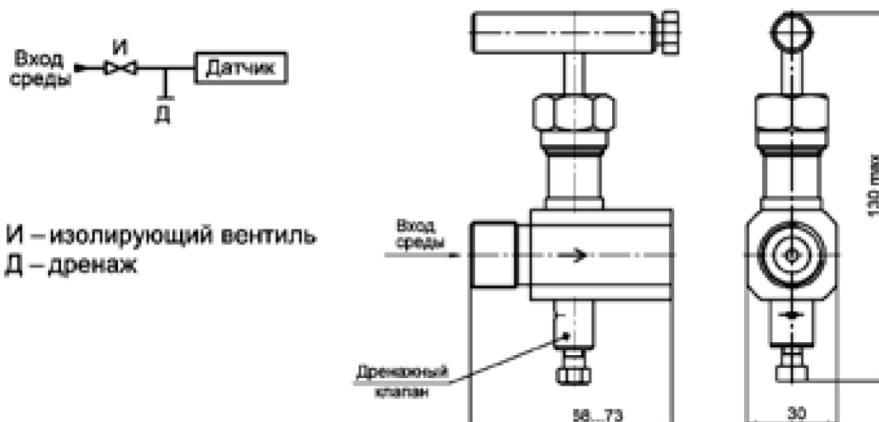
Схема и габаритные размеры одновентильного блока ВБ1.
